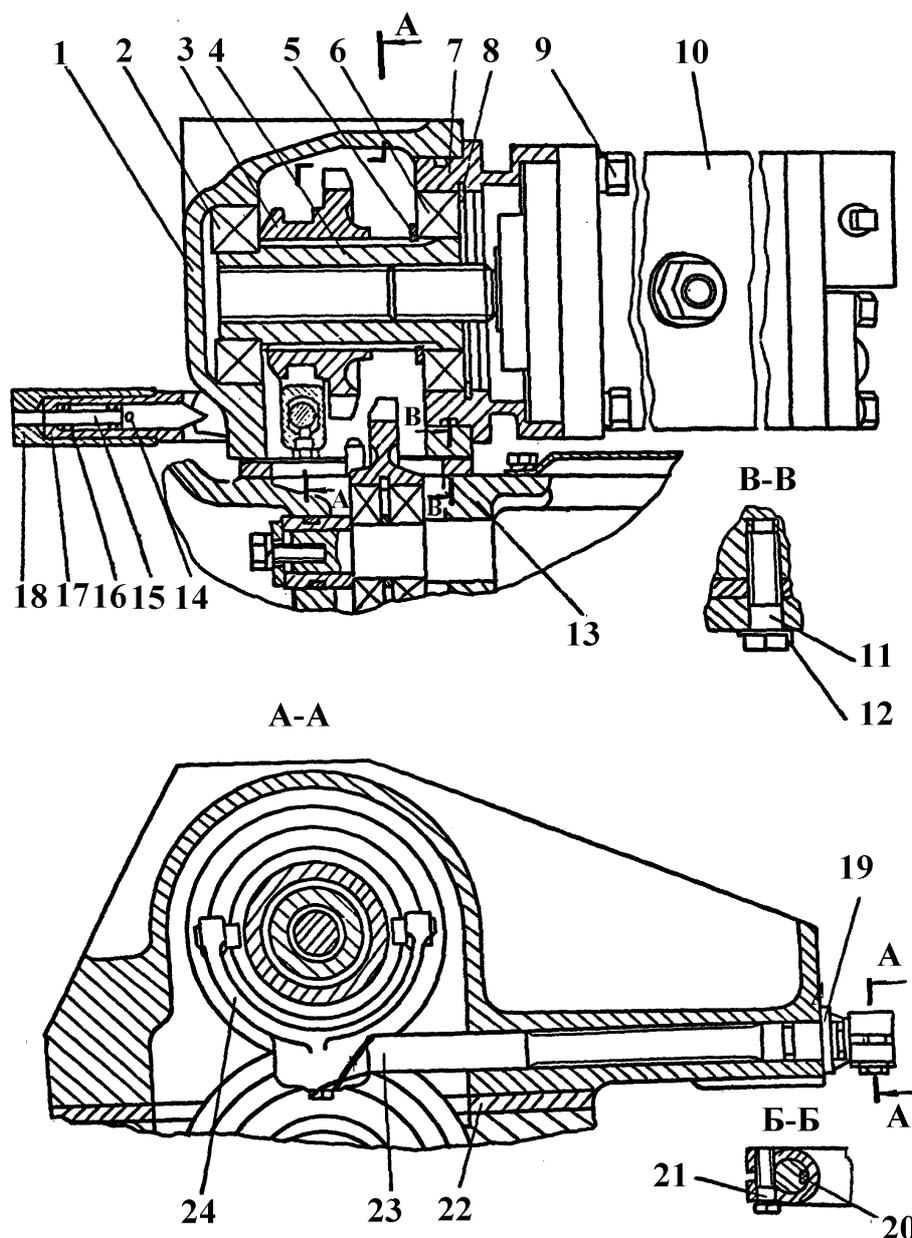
Привод насоса гидросистемы машины: 1 – корпус; 2, 6 – подшипники; 3 – шестерня; 4, 23 – валы; 5, 8 – стопорные кольца; 7 – приставка; 9 – гайка; 10 – гидронасос; 11, 21 – болты; 12 – отгибная шайба; 13 – корпус сцепления; 14 – штифт; 15 – фиксатор; 16 – пружина; 17 – рукоятка; 18 – стакан; 19 – пластина; 20 – шпонка; 22 – пластина; 24 – вилка
